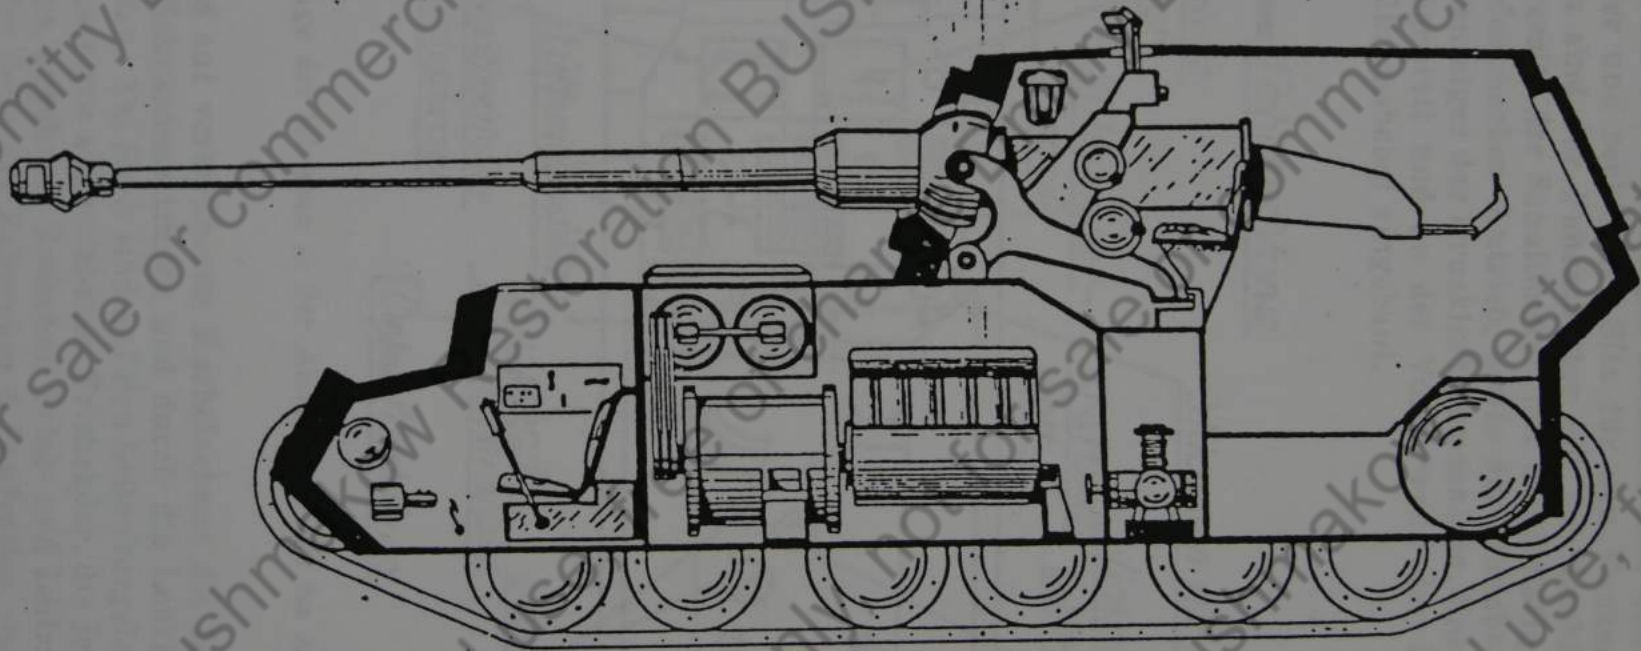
Aufbau des Panzerjäger Tiger (P) (Aufriß)
